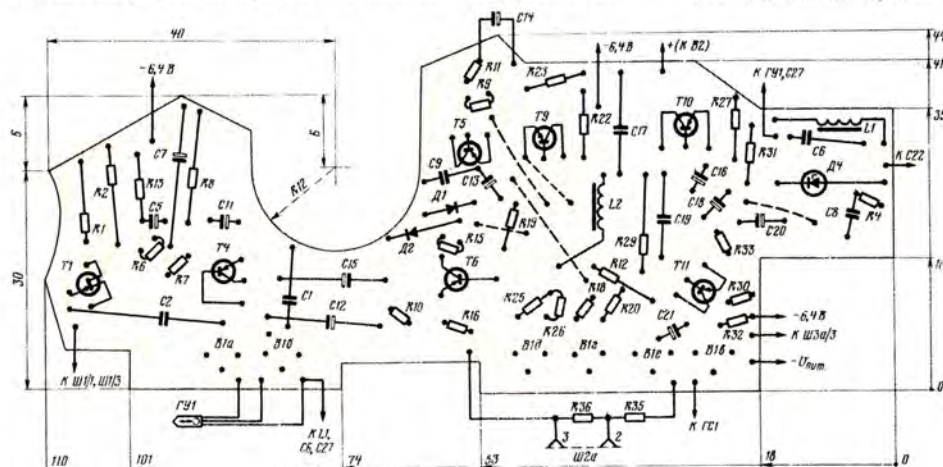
Печатная плата и схема соединений универсального усилителя.
